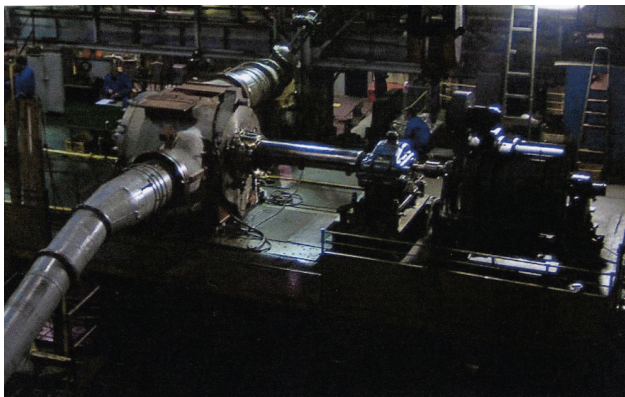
Компрессор НЦ-398 для КС «Шатровская»
